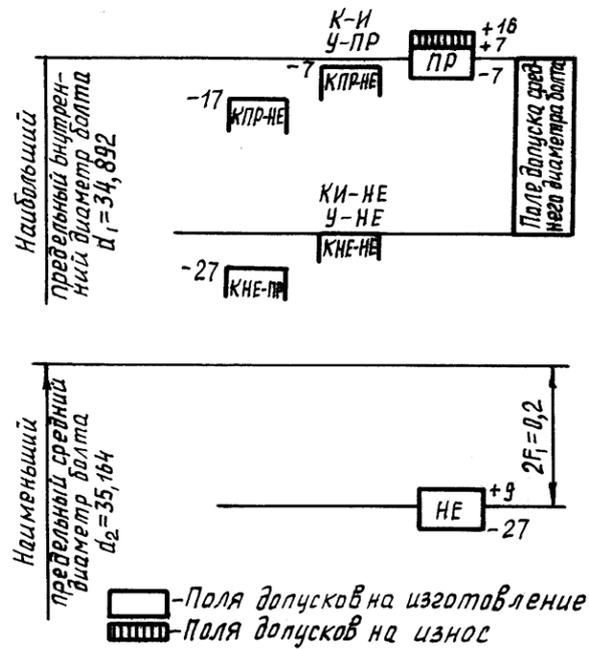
Схема расположения полей допусков внутреннего диаметра калибров для проверки болтов
